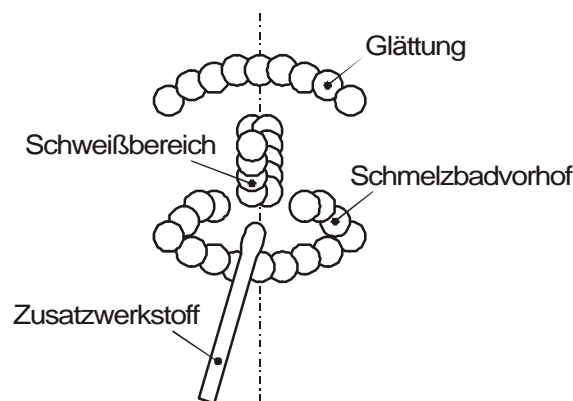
Ablenkraster zum Elektronenstrahlschweißen mit Zusatzwerkstoff [3.4.7]
